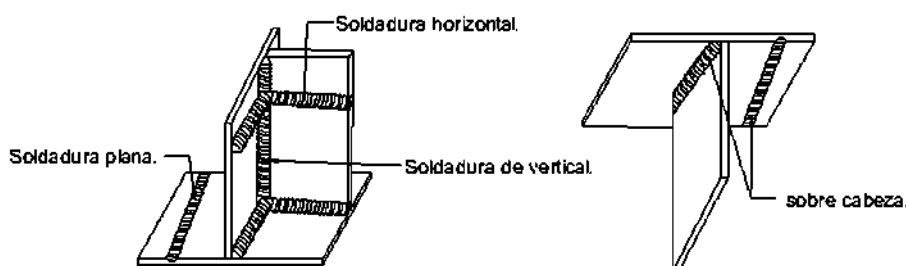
8 Posición de soldaduras (Modificado de Jack, C. & Stephen, F. 2012).
